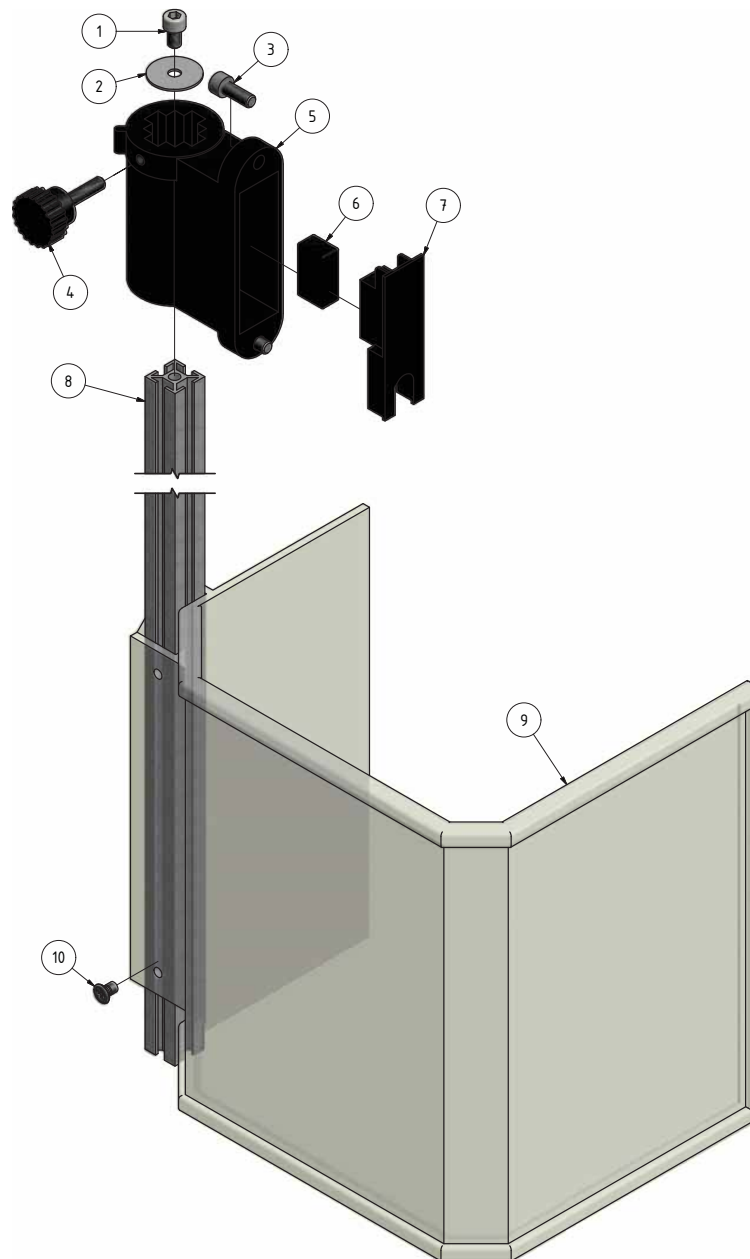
Bohrfutterschutz - Drilling chuck protection
